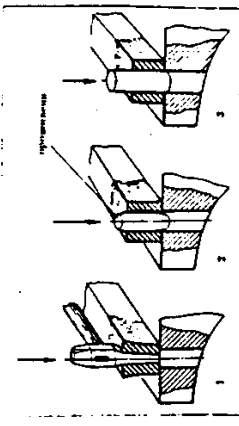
Пробивка отверстий: 1 — предварительная пробивка; 2 — пробивка бочкообразным прошивком; 3 — калировка
